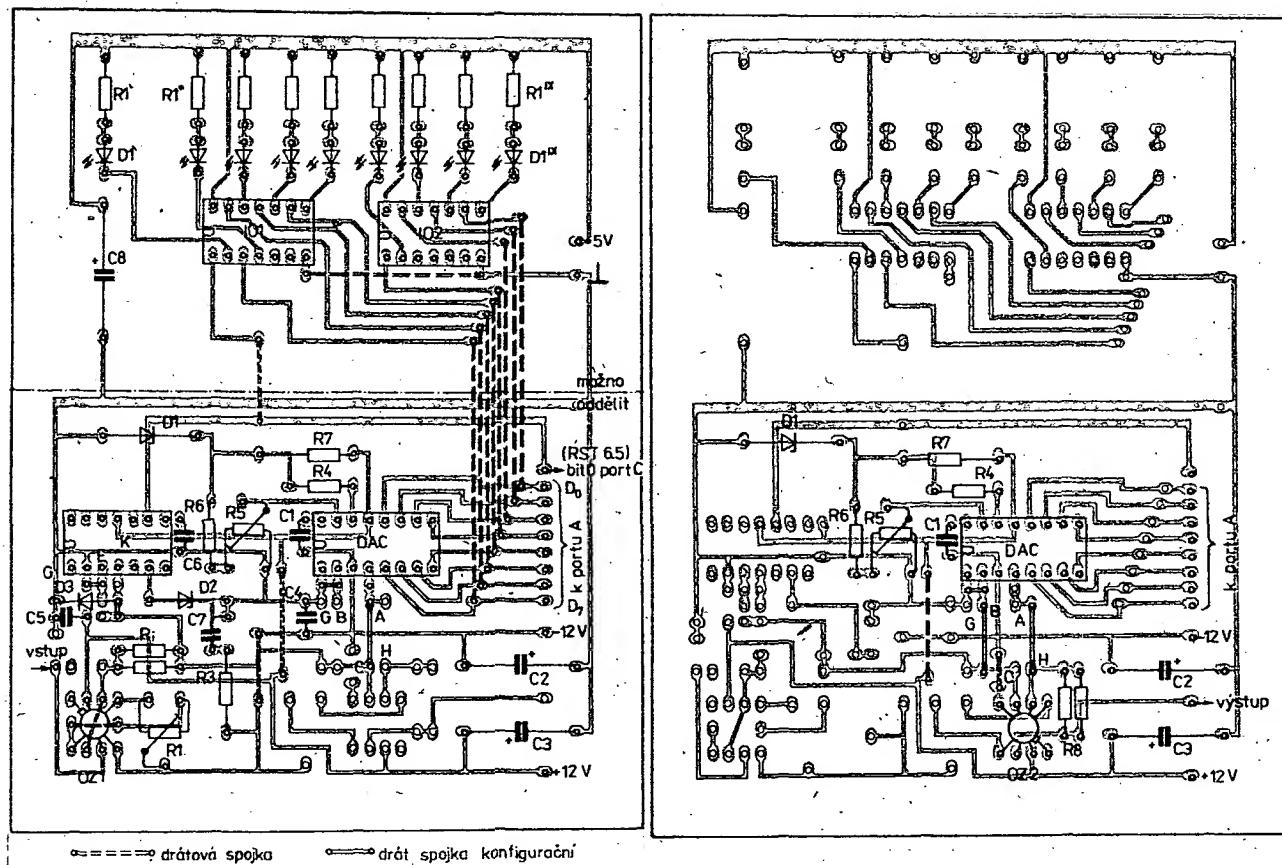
Zapojení univerzálního převodníku A/D a D/A s řízením účasti procesoru při převodu
